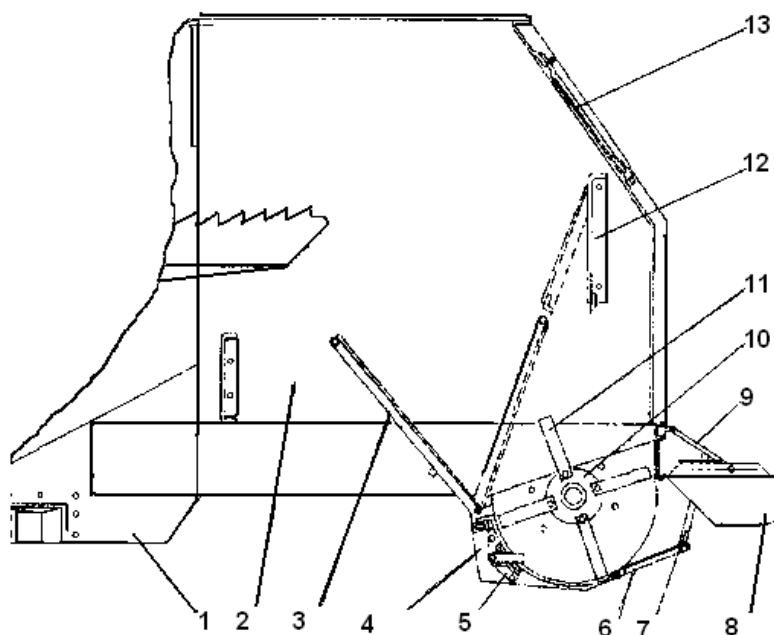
Измельчитель-разбрасыватель: 1 – рама; 2 – капот; 3 – щиток; 4 – поддон; 5 – брус ножевой; 6 – щиток направляющий; 7 – тяга; 8 – разбрасыватель; 9 – тяга; 10 – барабан измельчающий; 11 – нож пластинчатый; 12 – щиток; 13 – люк
